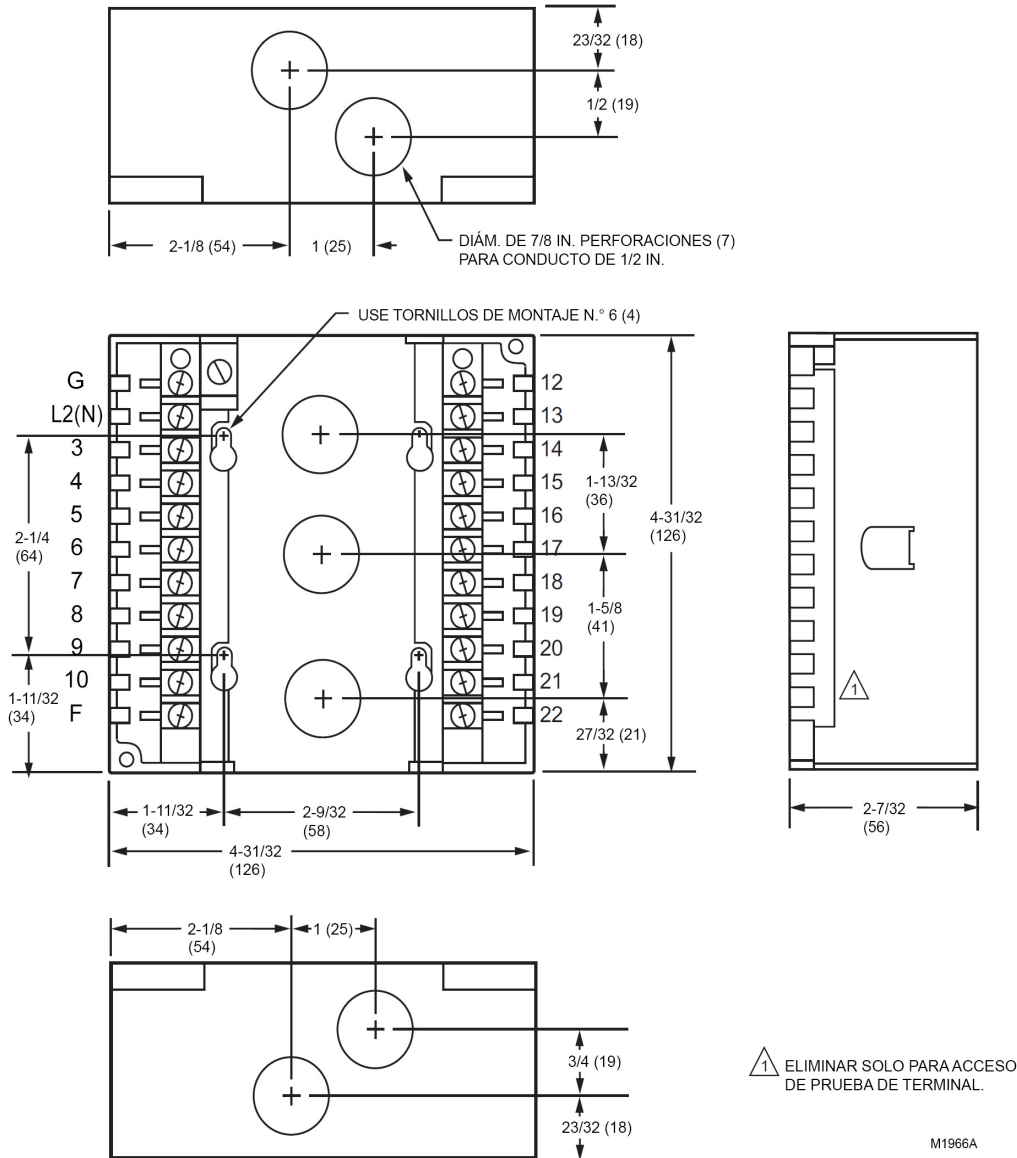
Vista superior y frontal de la subbase de cableado Q7800B1003 (4 caras) con dimensiones en pulgadas (mm).
